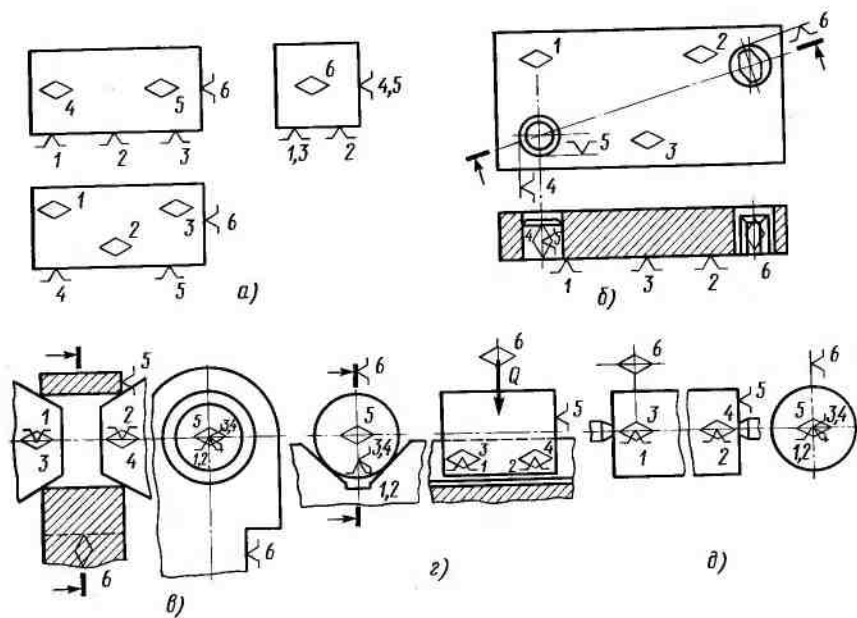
Схемы базирования заготовок в приспособлениях: а — базирование в «координатный угол», б — по плоскости и двум отверстиям, в — по главному «черному» отверстию, г — в призме, д — в центрах
